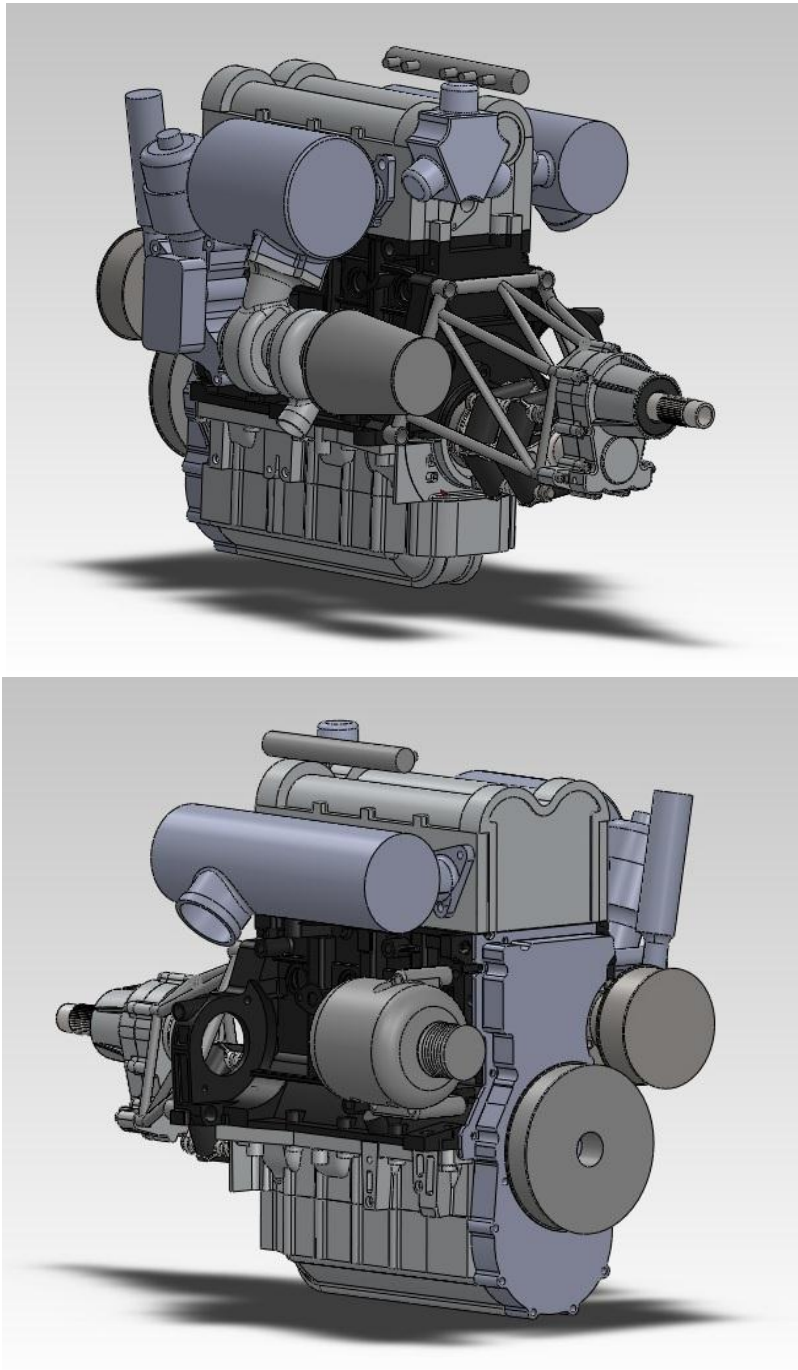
Assieme del motore completo di tutti gli accessori compreso il riduttore.
